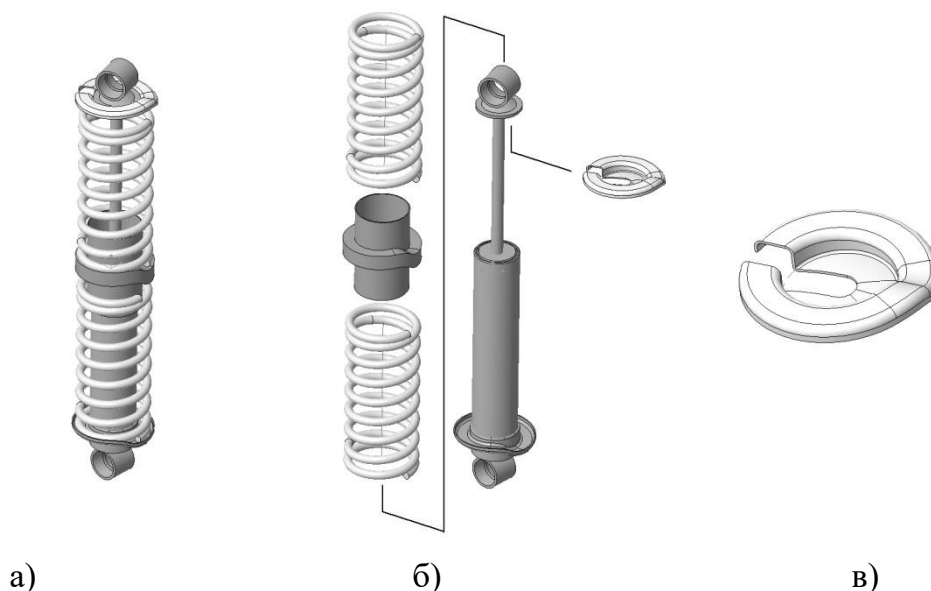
Конструкция стойки подвески: а) стойка в сборе; б) процесс сборки стойки (разнесённый вид); в) закладная верхняя опора пружины
